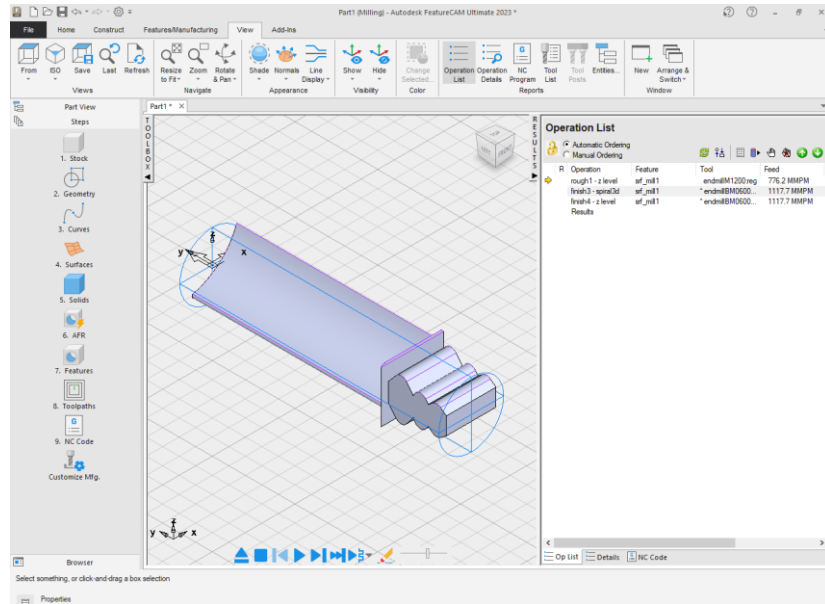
Вибір форми заготовки для лопатки газотурбінного двигуна
